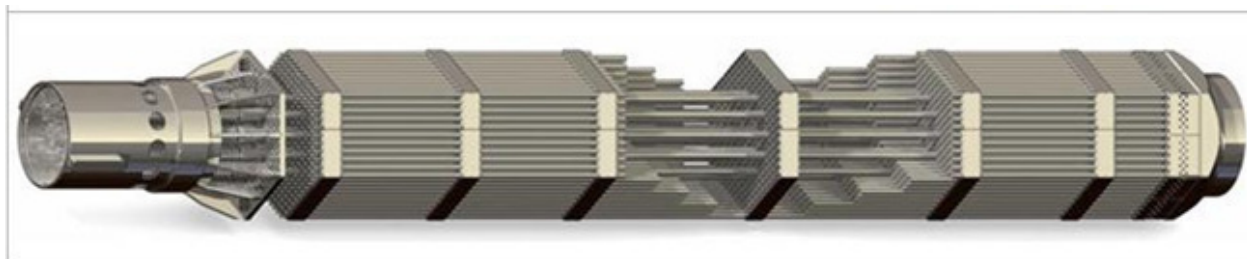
Общий вид ТВС реактора ВВЭР-1000 типа ТВС-2М
